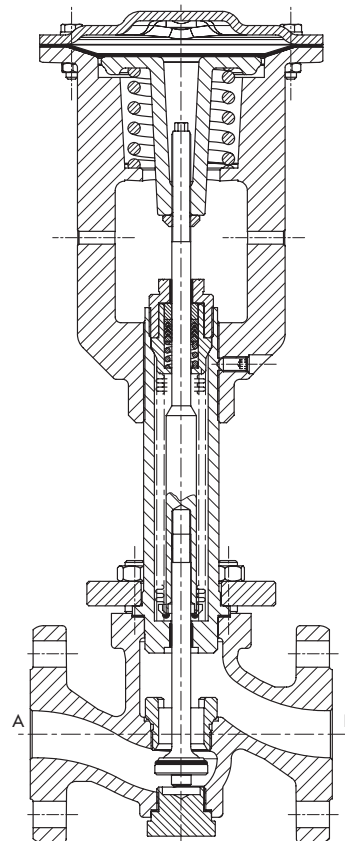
Pneumatisches Auf/Zu-Ventil Typ 3351 · Balgausführung
